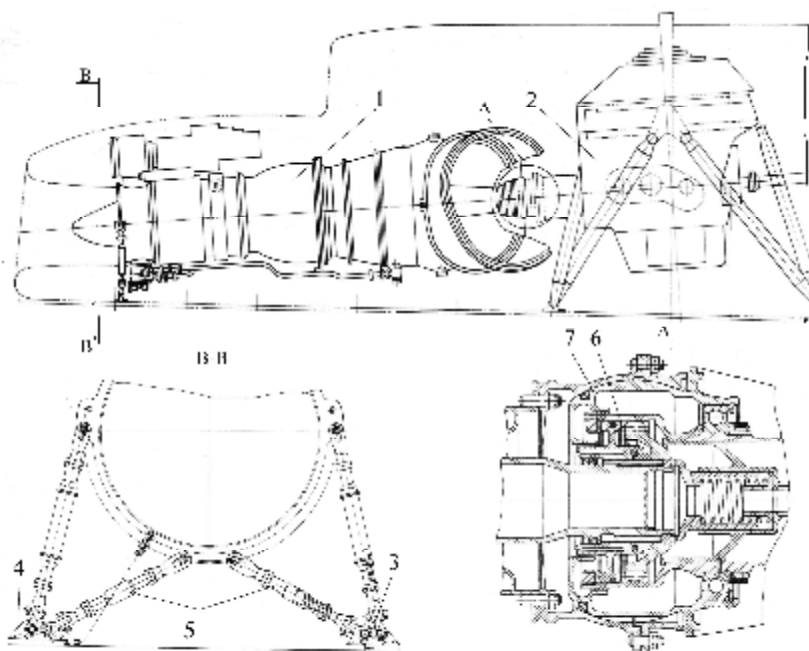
Конструкция крепления двигателя с шаровой опорой на главном редукторе.
